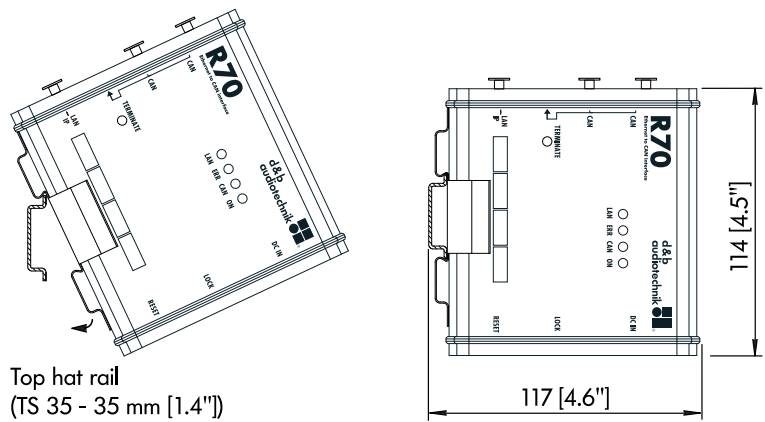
montage sur rail oméga avec dimensions en mm [inch]
